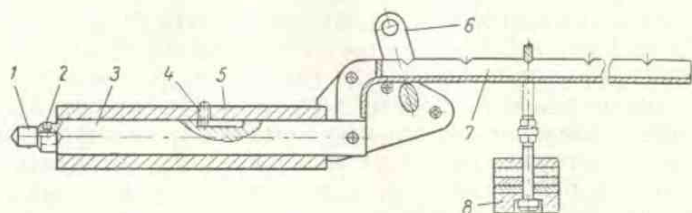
Схема приспособления к токарному станку для нанесения царапин на цилиндрические образцы:
